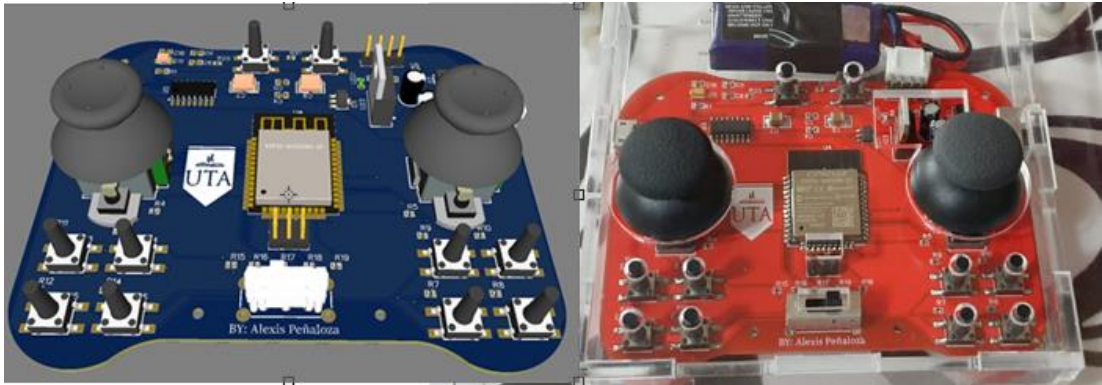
Diseño 3D en EasyEDA y la placa real soldado todos los elementos
